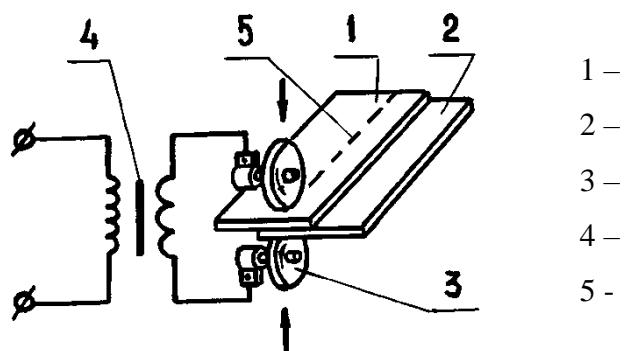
3 – Принципиальная схема роликовой сварки
